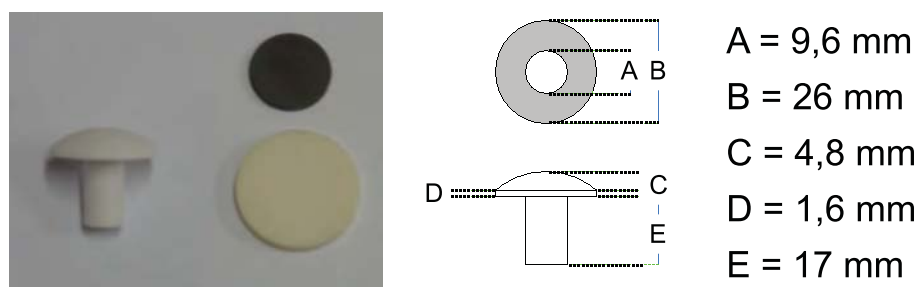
Forme ou/et dimensions des disques et des frotteurs utilisés dans cette étude.
